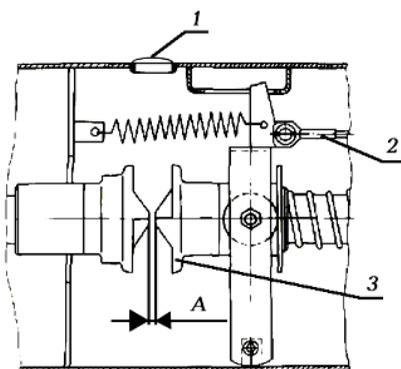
Схема регулировки кулачковой муфты привода:
